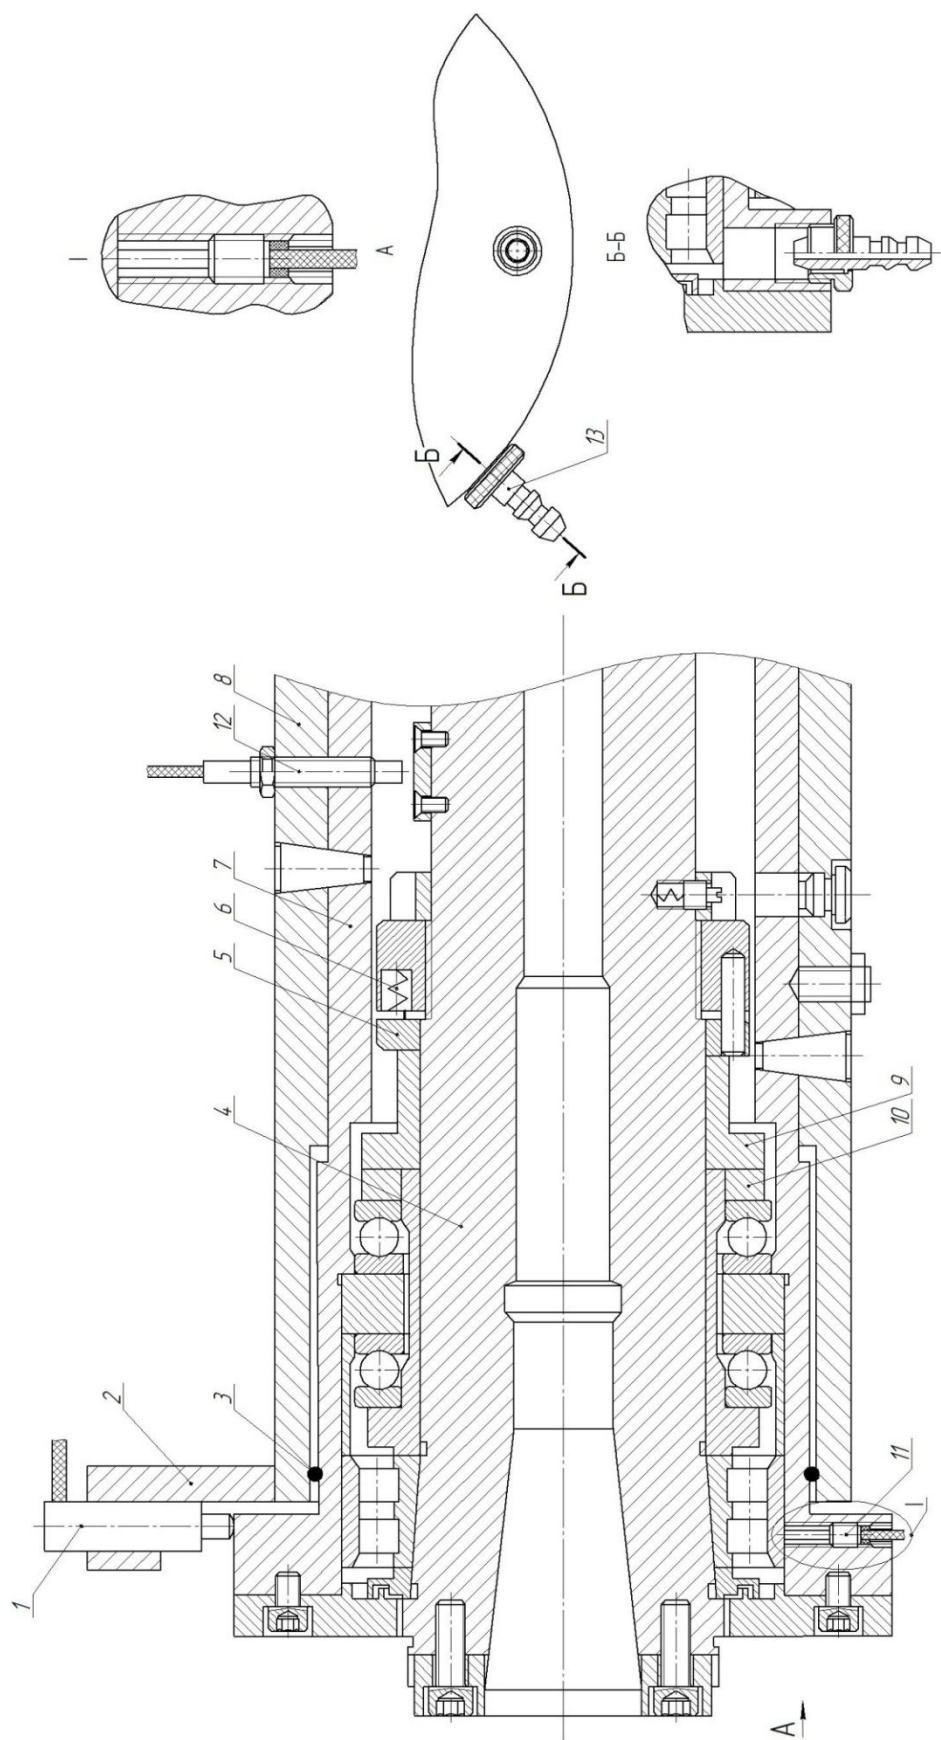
Шпиндельный узел фрезерного станка с динамометром
